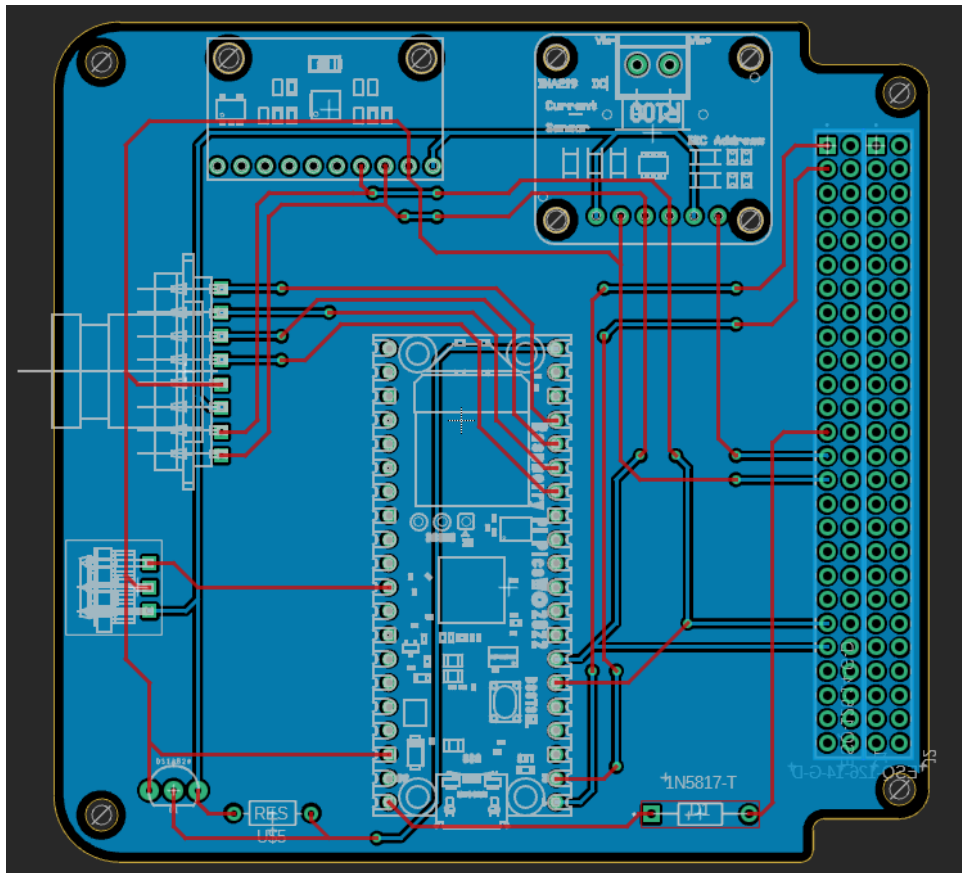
Diseño del PCB para el ensamblaje del OBC.
